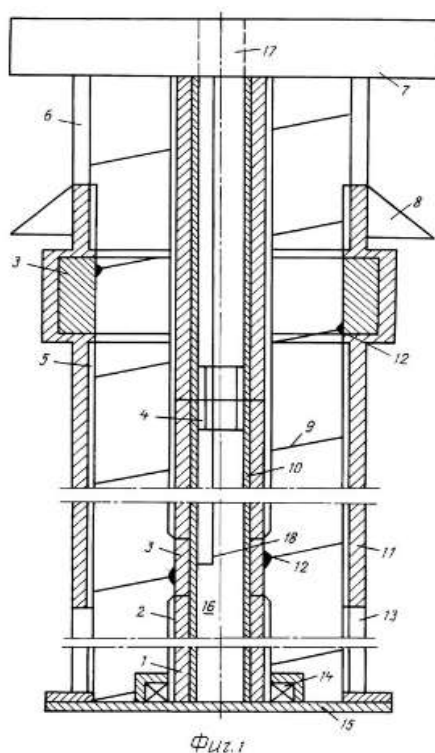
Шнековый транспортер с расположением редуктора
